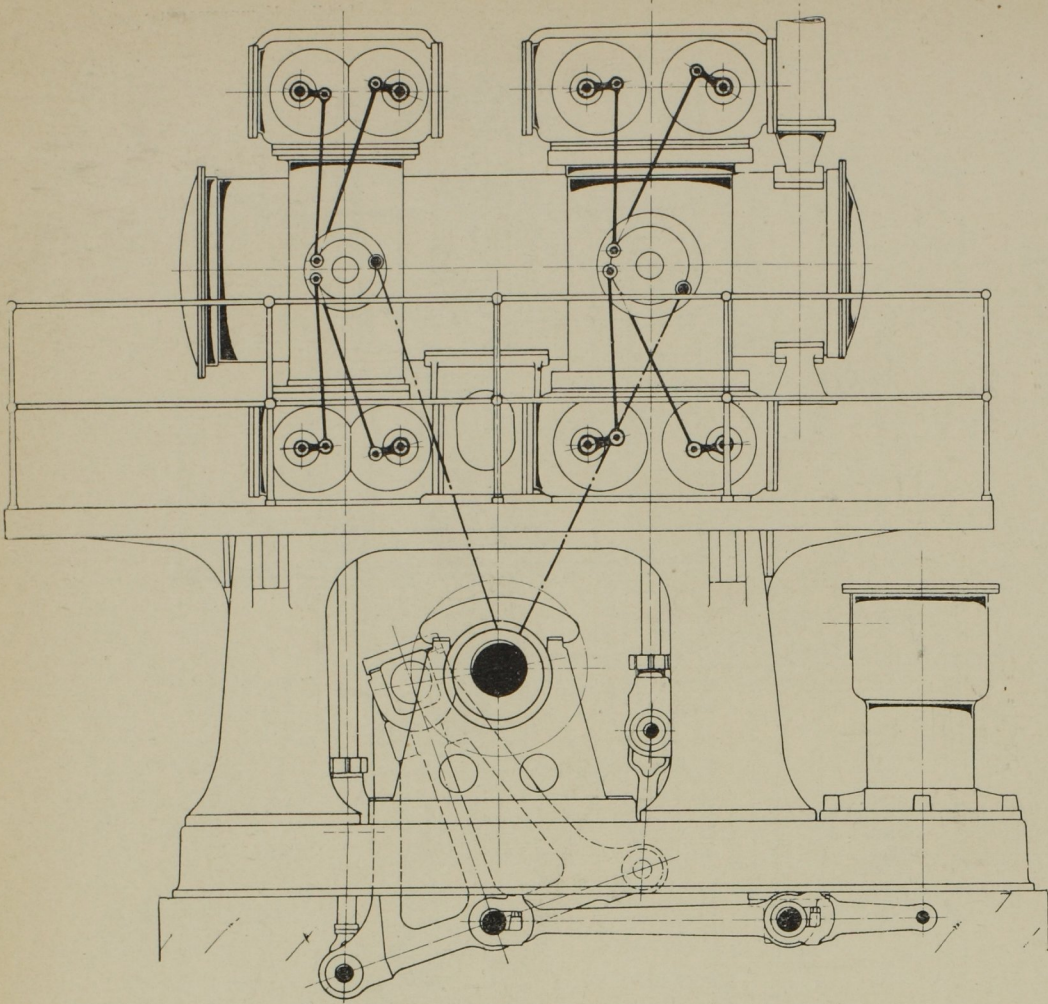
Seitenansicht des Kompressors. Massst. 1:36.
